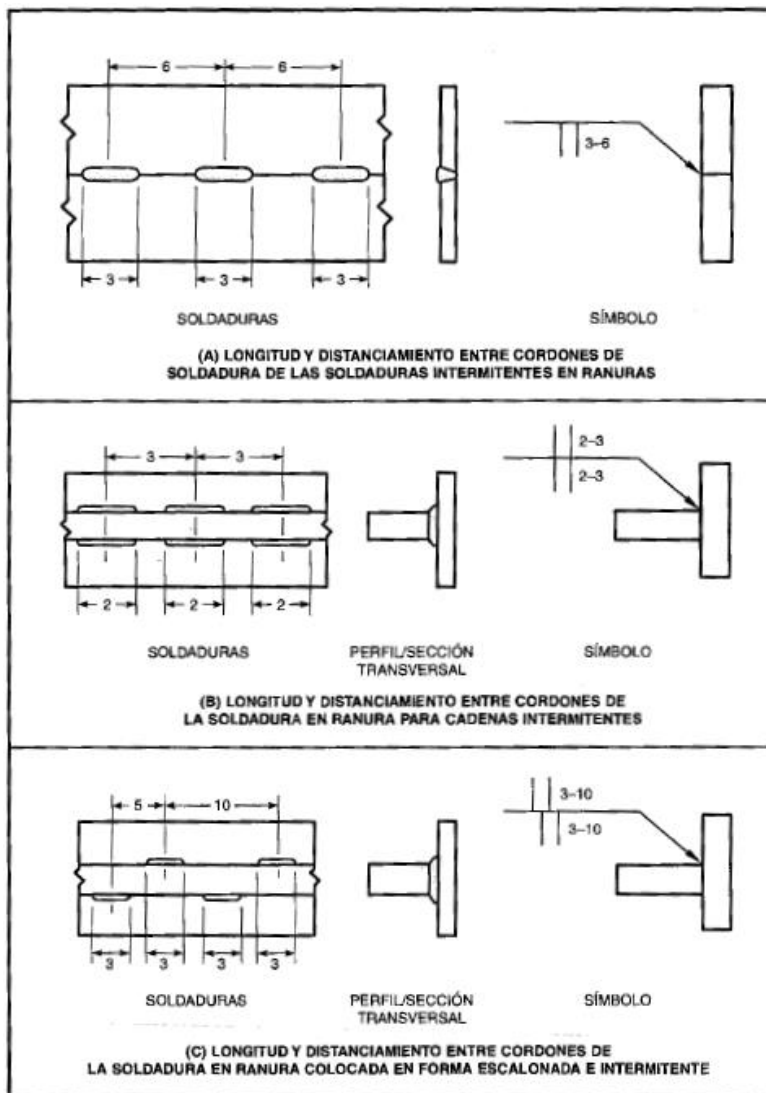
Aplicaciones en la Soldadura de Forma Intermitente. [15]
